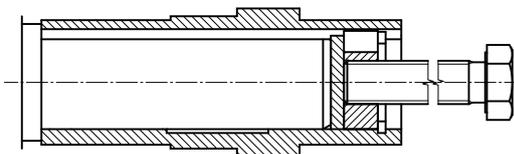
Redutor fixo com elemento de fixação sobre eixo com face de encosto
